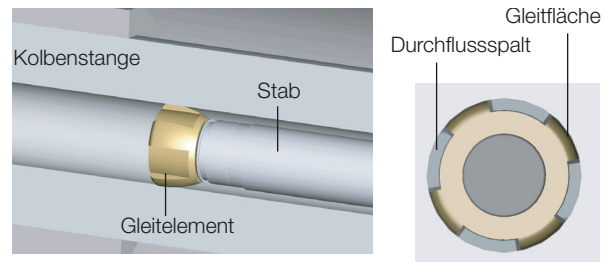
Detailansicht und Draufsicht Gleitelement
